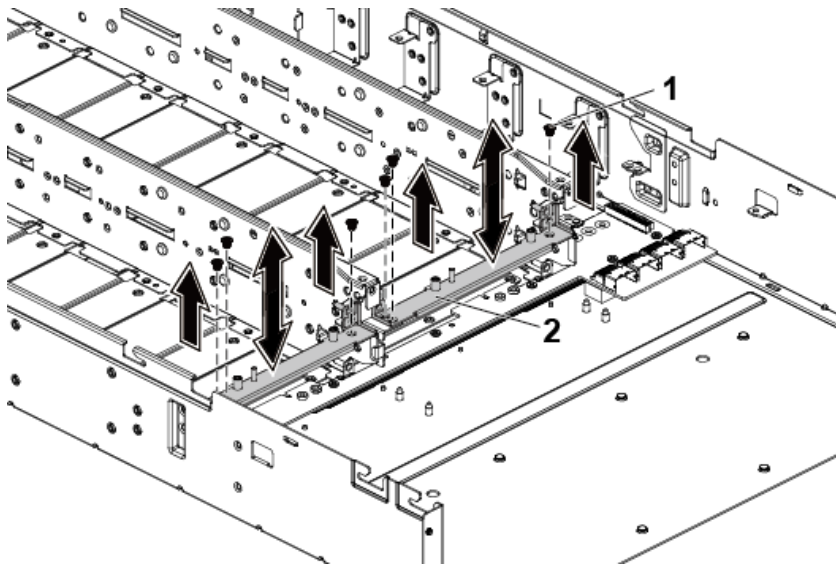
Entfernen und Einbauen der Mittelplattenhalterung
